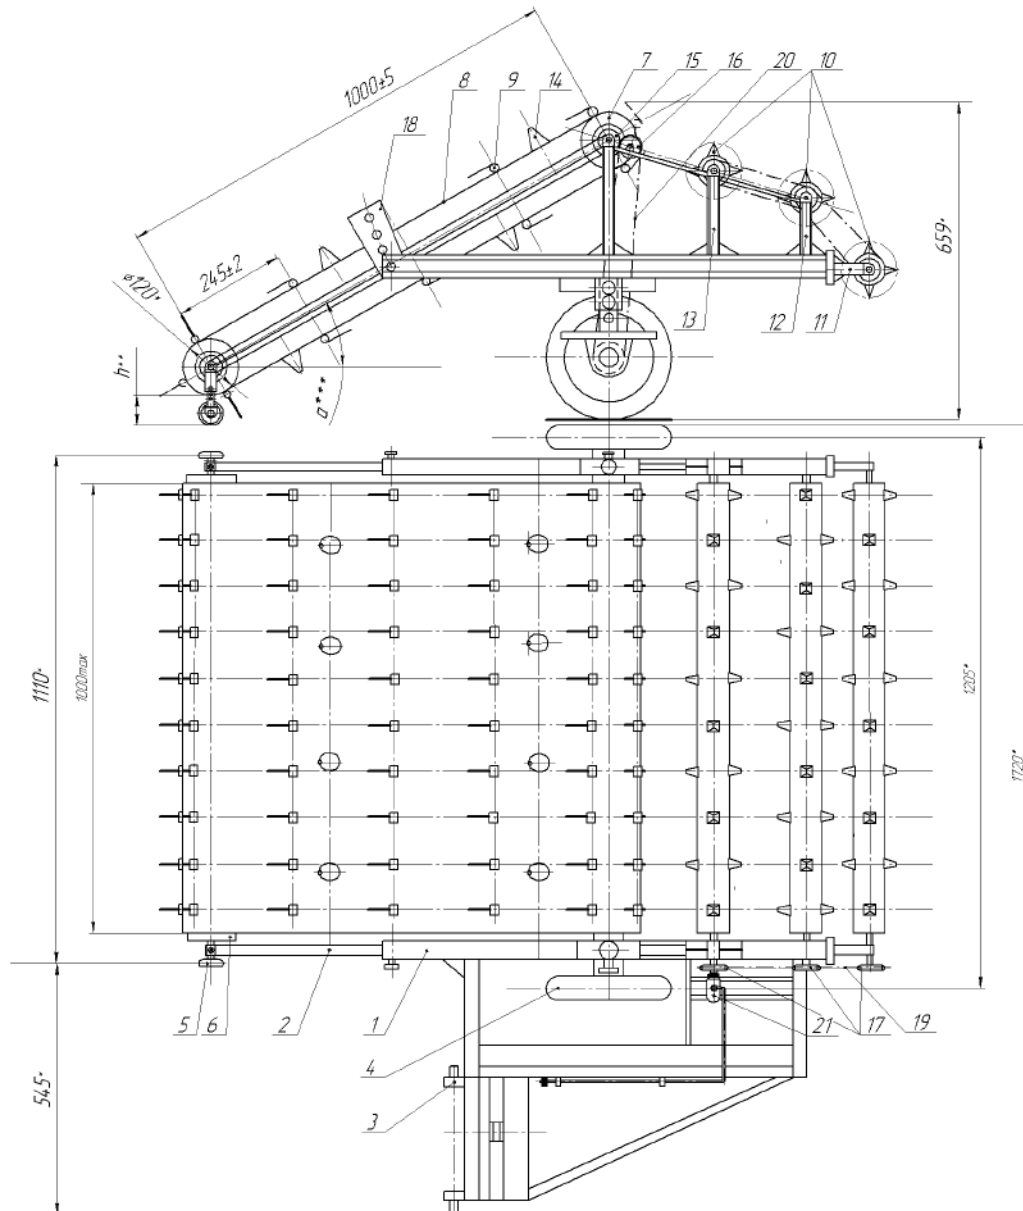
Конструктивно-компонувальна підбирача-розпушувача валків льону: 1- базова рама; 2- рама підбирального вузла; 3- навіска; 4, 5- опорні колеса; 6- ведений барабан; 7- ведучий барабан; 8- тягова стрічка; 9- зуби; 10- бітер; 11,12,13- опори; 14- вловлювач; 15- шестерня; 16,17- зірочки; 18- сектор; 19,20- ланцюг; 21- гідромотор
